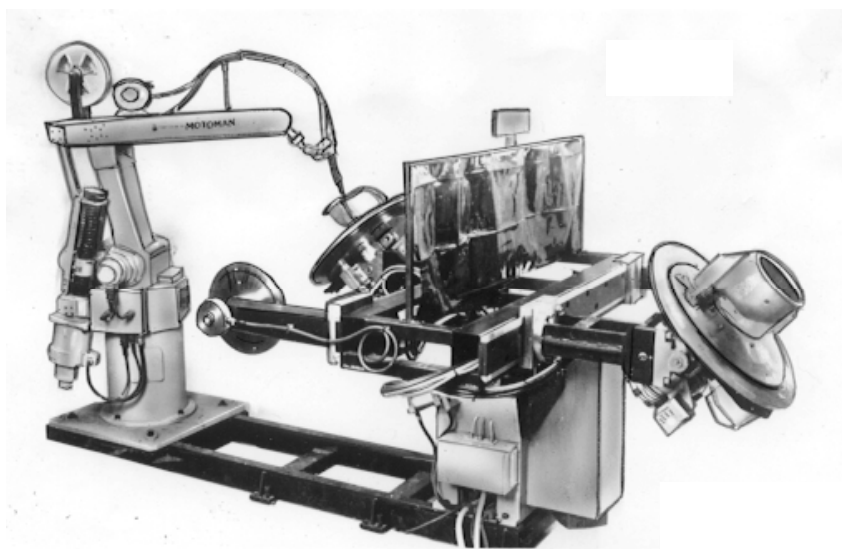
Робототехнический комплекс для дуговой сварки с ПР «Мотоман» с двухкоординатным столом.
